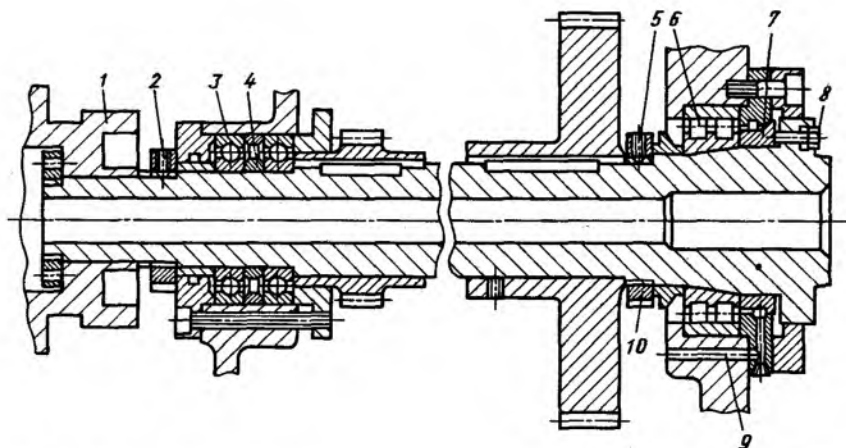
Шпиндель с опорами токарно-револьверного полуавтомата 1М425
